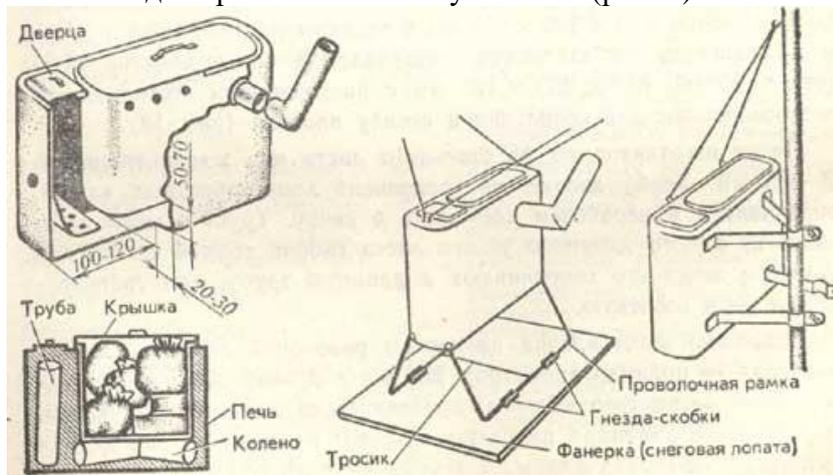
Печь для варки пищи, ее установка и транспортное положение
